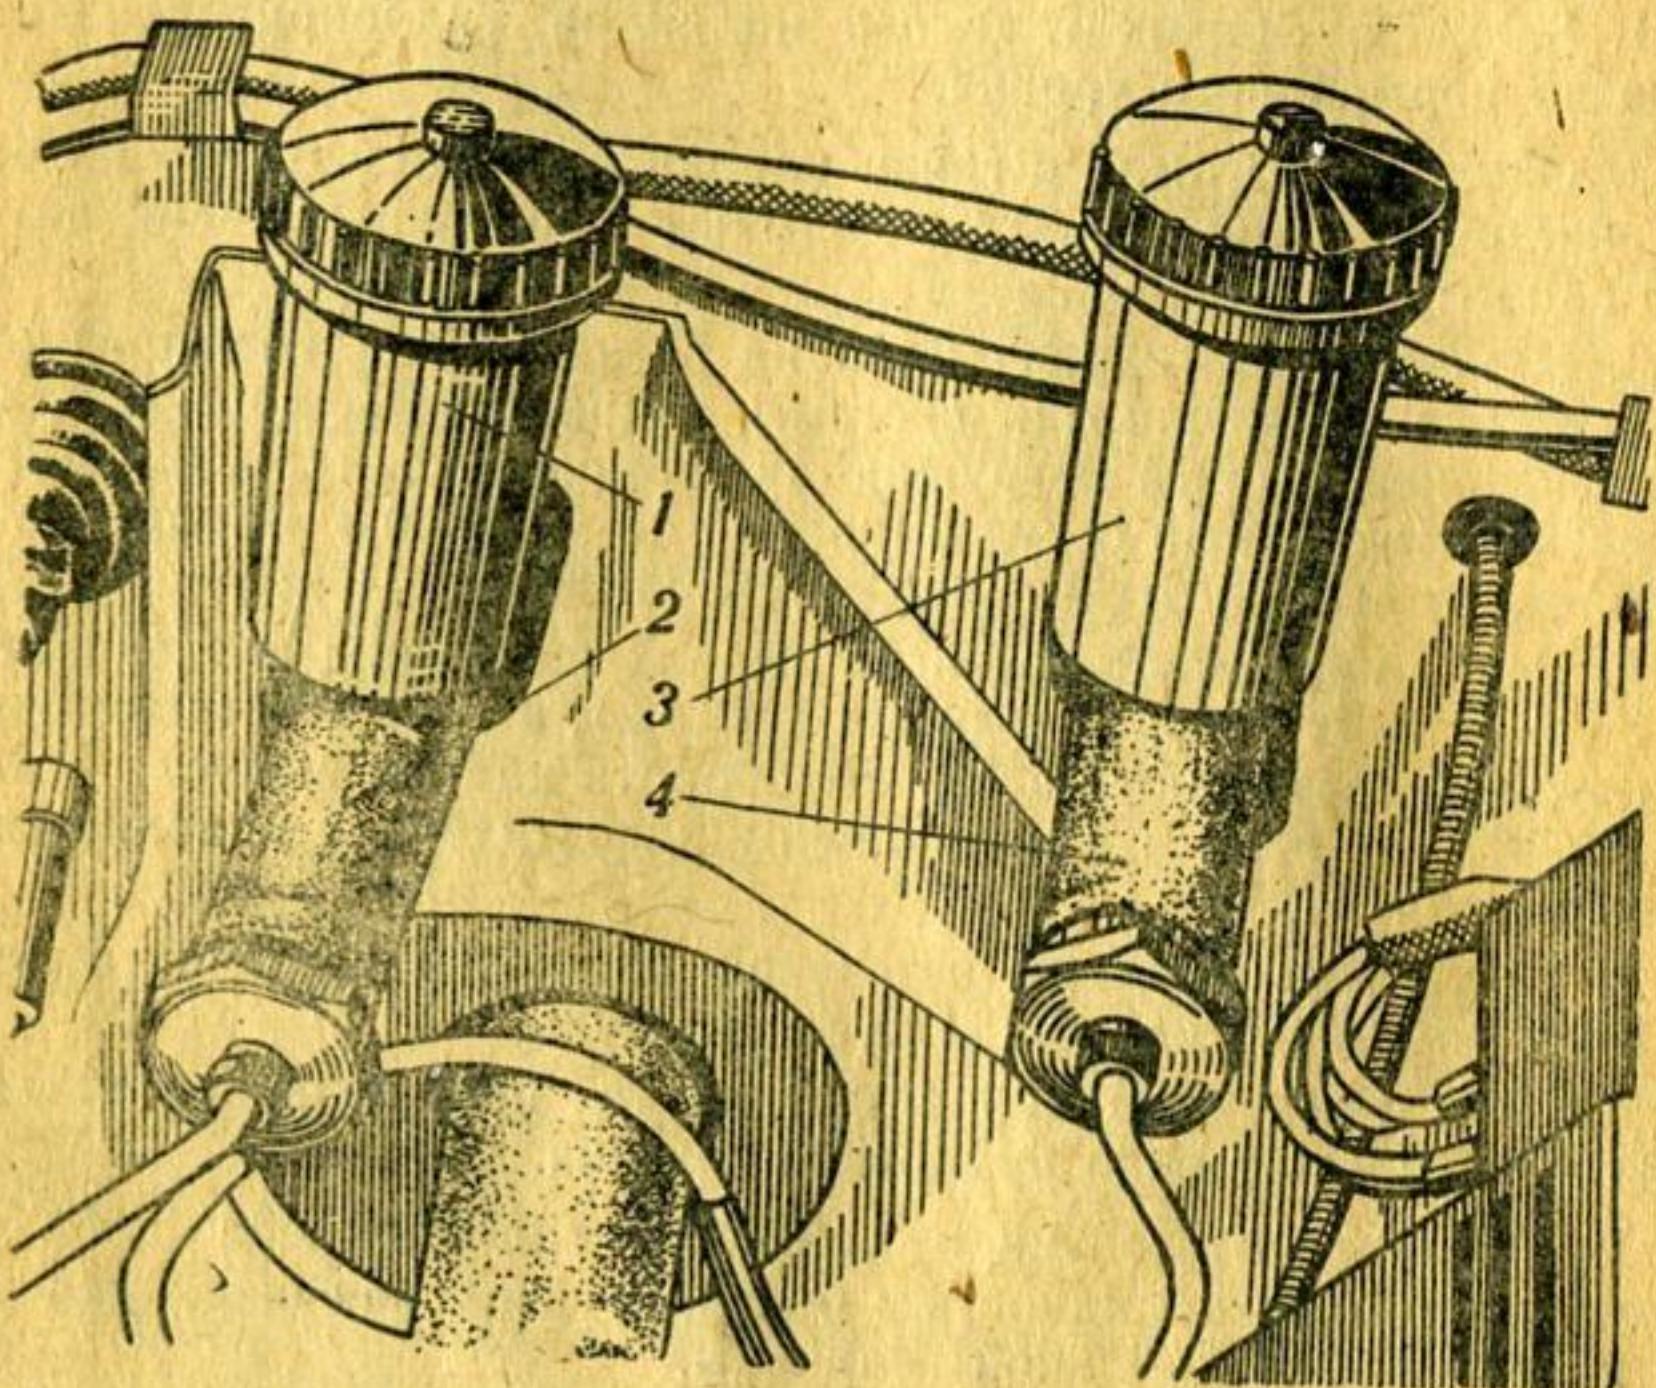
Расположение главных цилиндров гидропривода ножного тормоза и сцепления:
